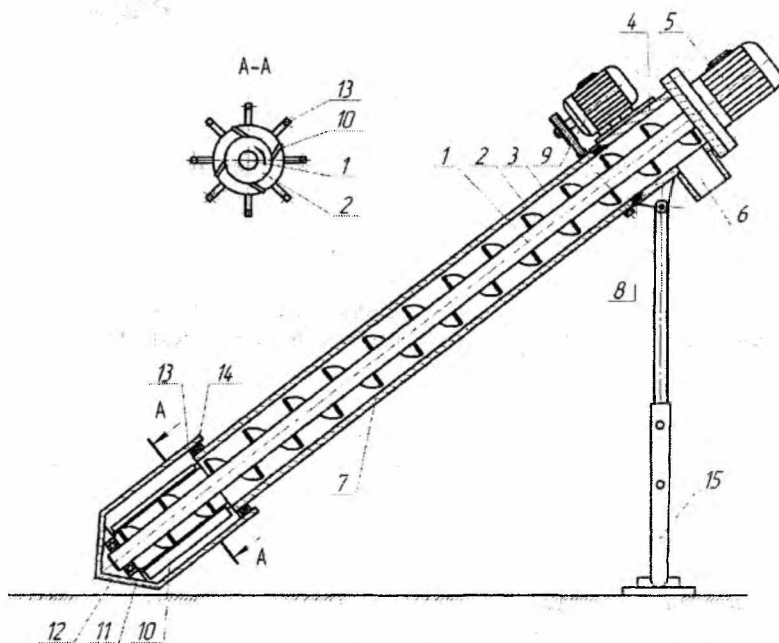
Конструкційна схема гвинтового конвеєра із обертовим кожухом
